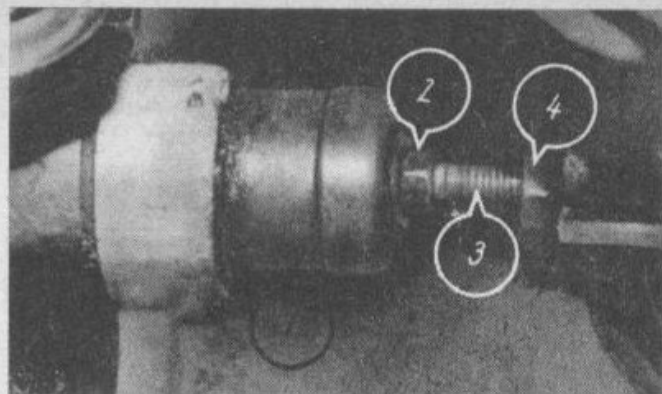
Kupplungsarbeitszylinder mit 1 – Schutzkappe, 2 – Sechskant SW 10 mm, 3 – Druckstößel mit Gewinde, 4 – Gegenmutter SW 14 mm
